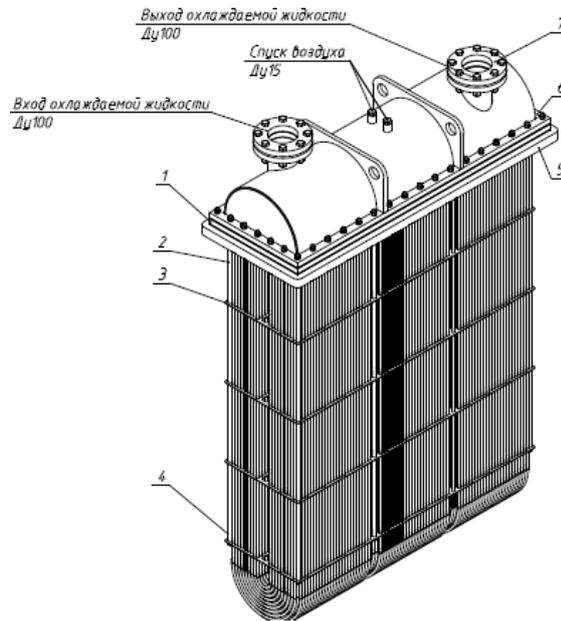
Чертеж общего вида судового охладителя погружного типа
